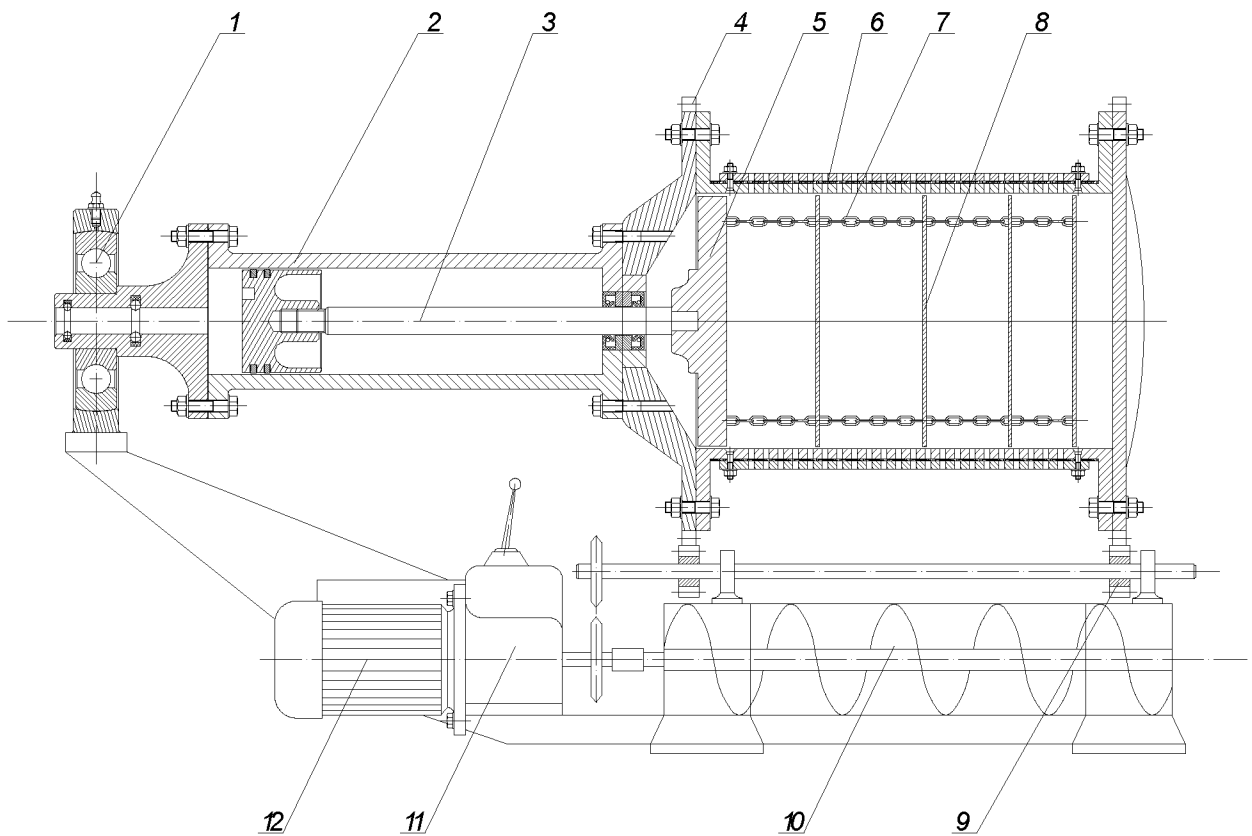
Схема корзинного преса: 1 – підшипниковий вузол;
